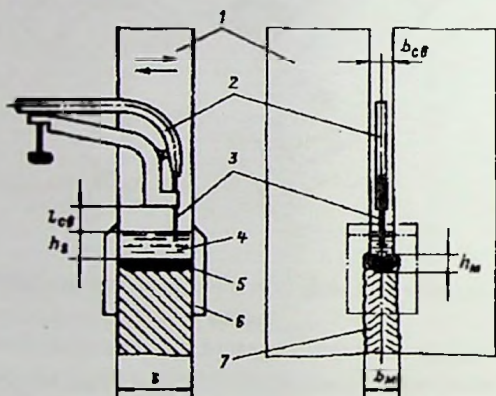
Схема электрошлаковой сварки:
